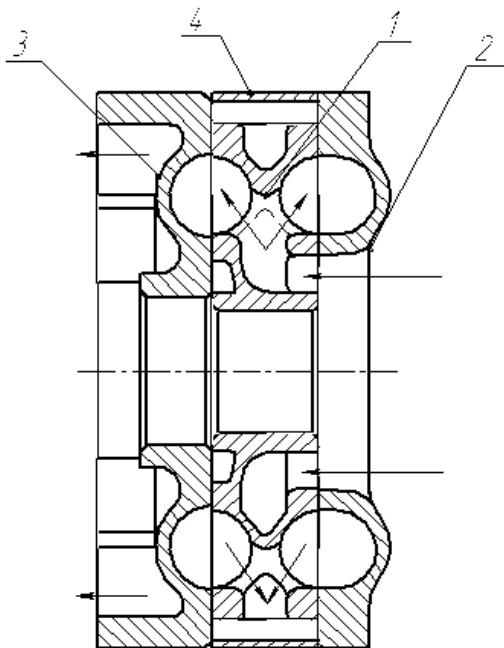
Загальний вид ступені: 1 – робоче колесо; 2 – передня вихрова ступень; 3 – задня вихрова ступень; 4 – корпус робочого колеса
